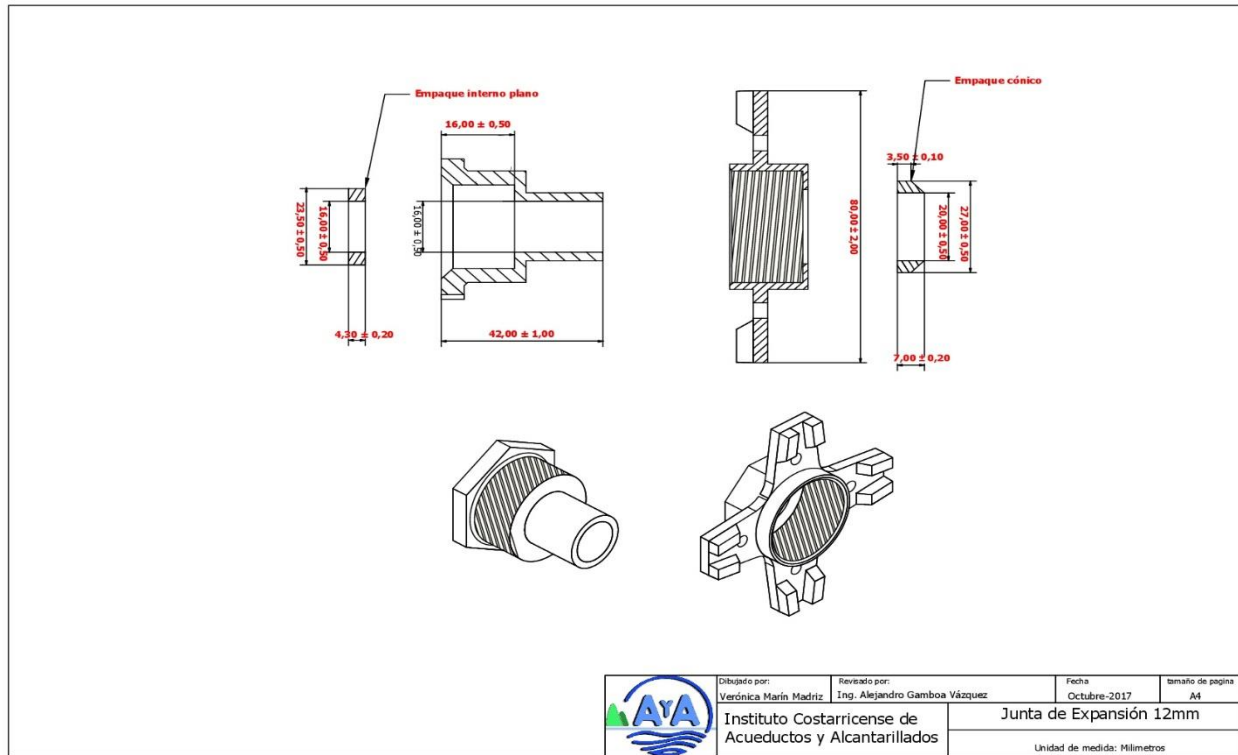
Plano de junta de expansión. Fuente: propia (marzo 2020).
